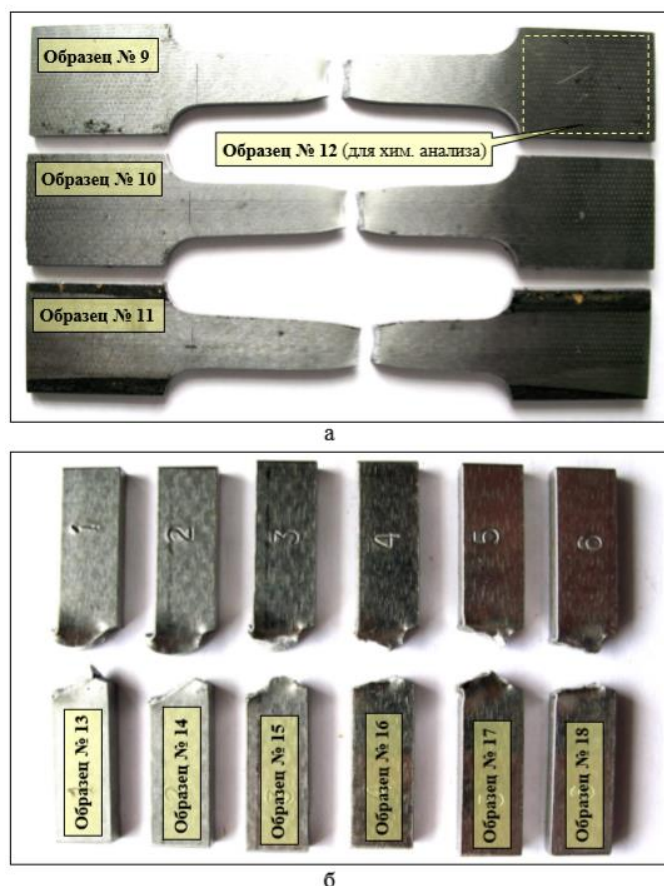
Общий вид образцов для испытаний: а - образцы для испытаний на растяжение; б - образцы для испытаний на ударный изгиб.
